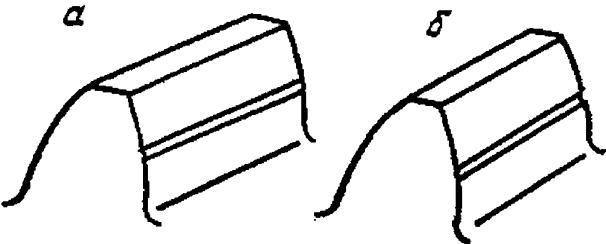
Образование хребта и впадины на сопрягаемых зубьях колеса и шестерни:
